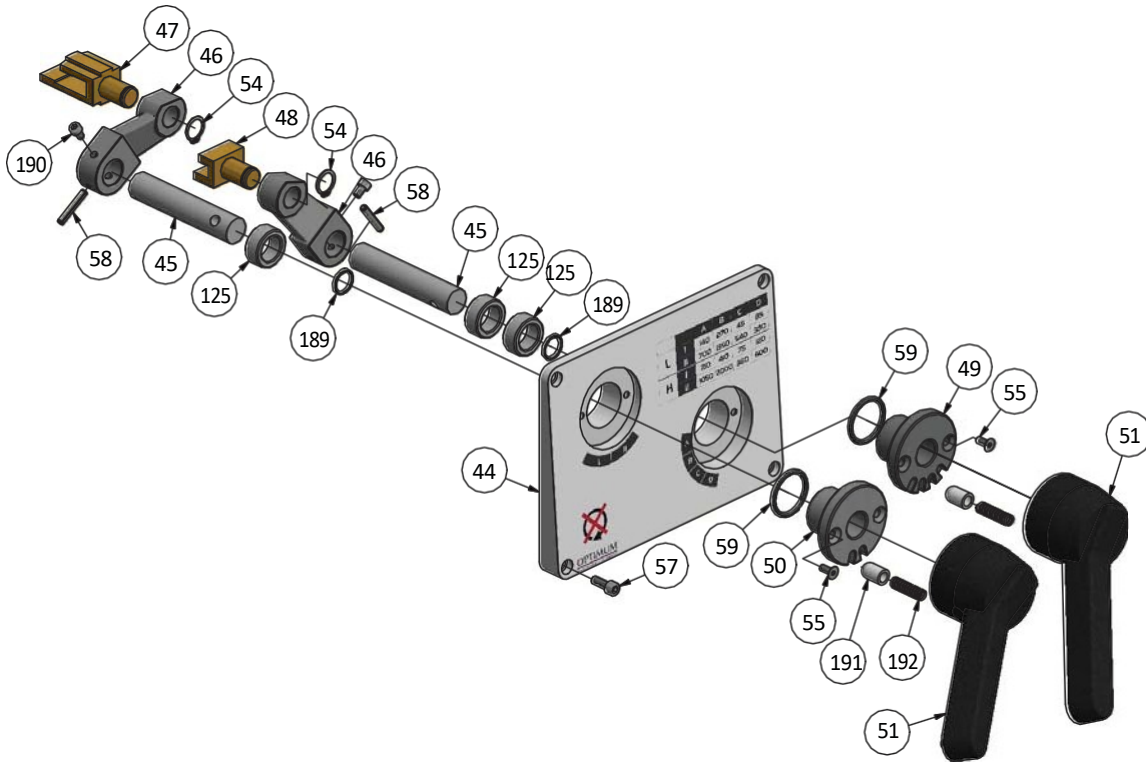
Getriebe Teil B - Section B de l'engrenage
